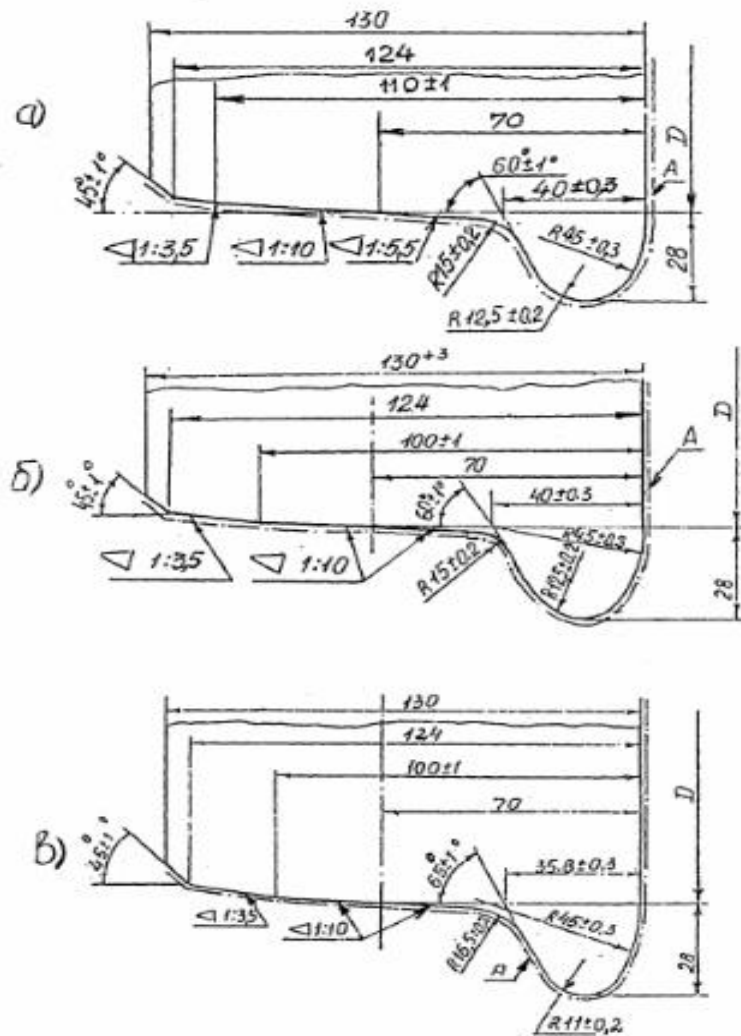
Профілі поверхні кочення обробленого ободу колеса:
